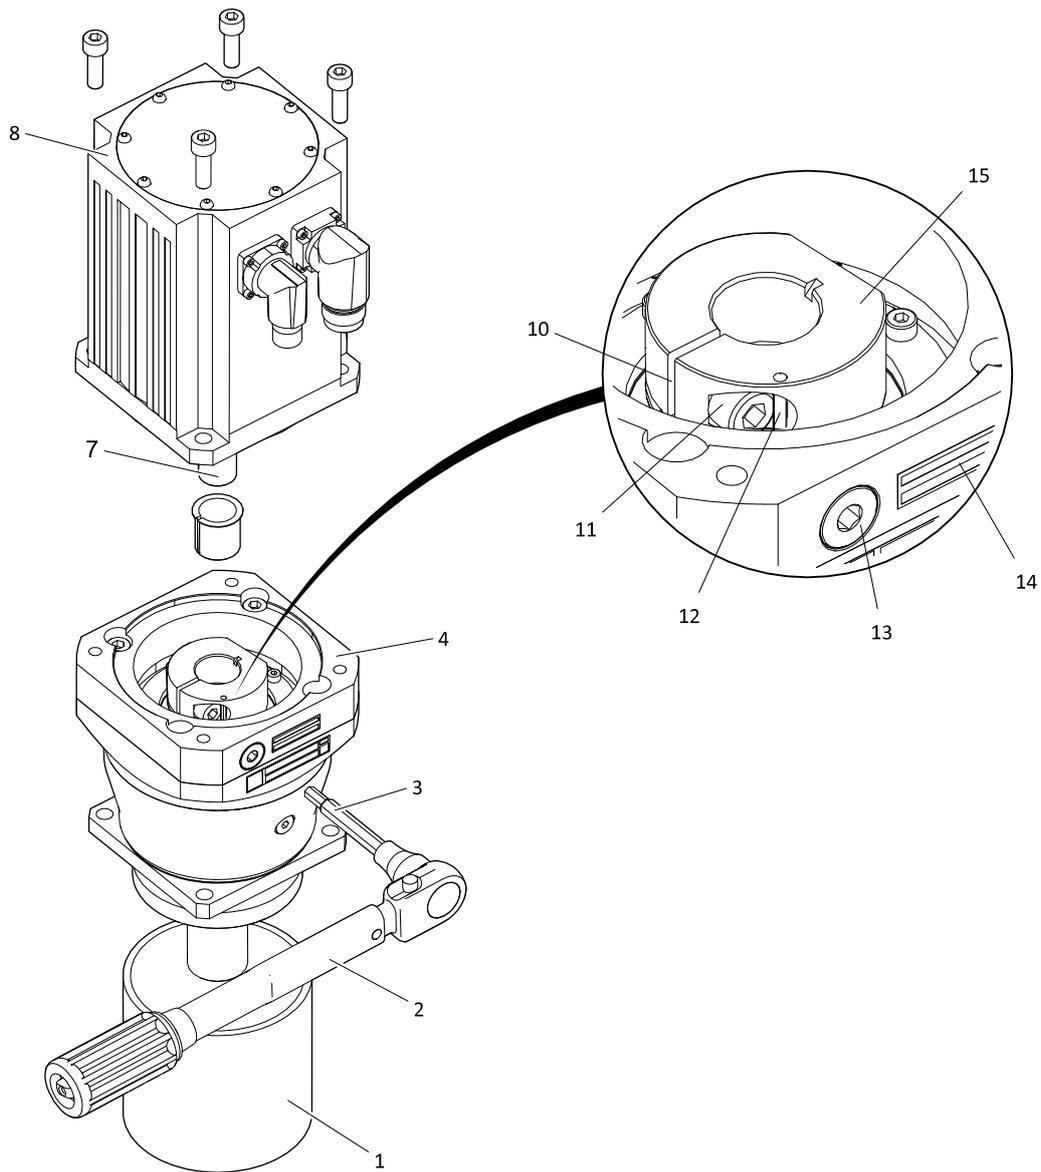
Montage eines Motors an ein Planetengetriebe P mit Motoradapter ME (Beispiel)
